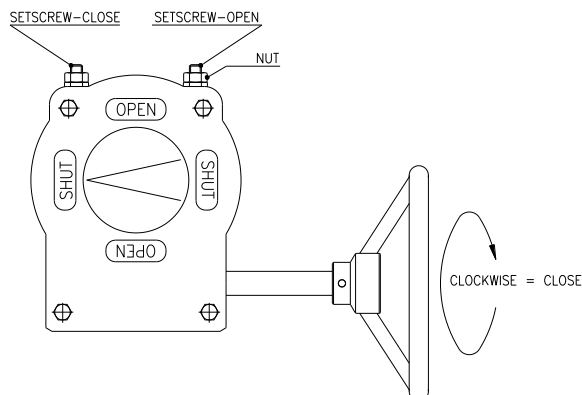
Einstellung der Stellschrauben für linkshändige Getriebe
